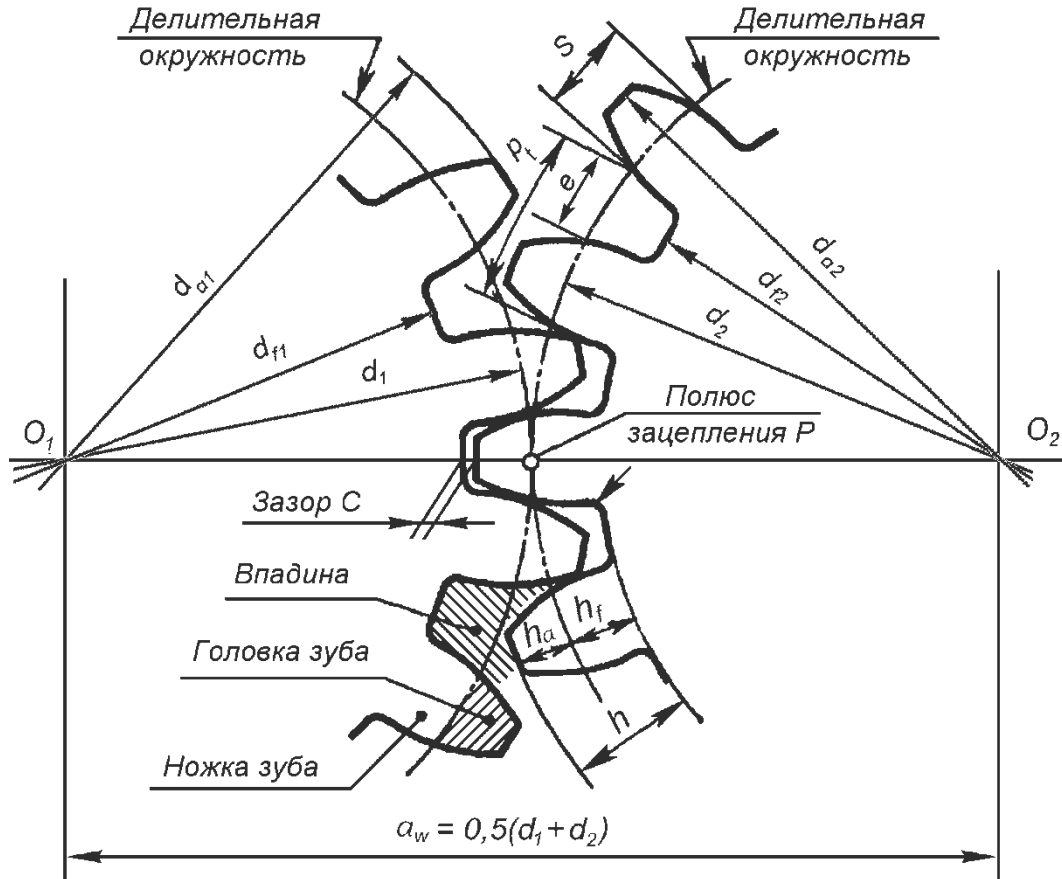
Основные параметры и обозначения элементов зубчатой передачи
